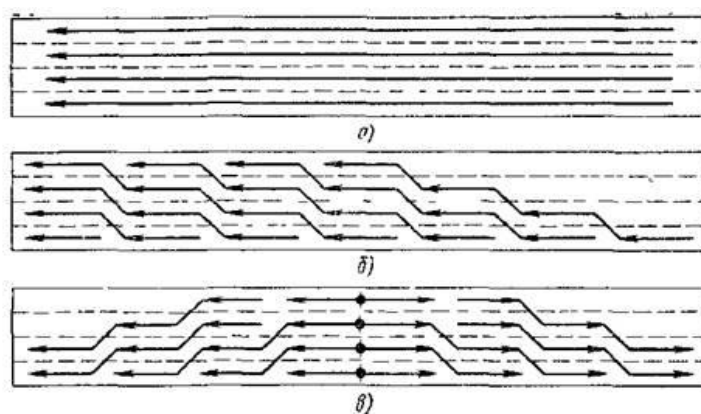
Последовательность выполнения многослойных швов при ручной и полуавтоматической сварке:
